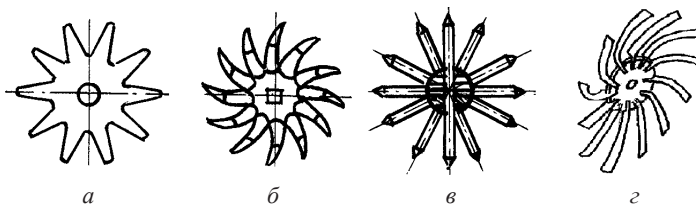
Рабочие органы ротационных борон: а – рыхлительный диск; б – игольчатый диск; в – зубовой диск; г – диск с загнутыми пластинчатыми зубьями
